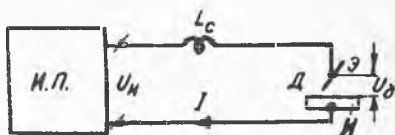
Схема энергетической системы при дуговой сварке; И. П. — источник питания; Д — сварочная дуга; Э — электрод; И — изделие
